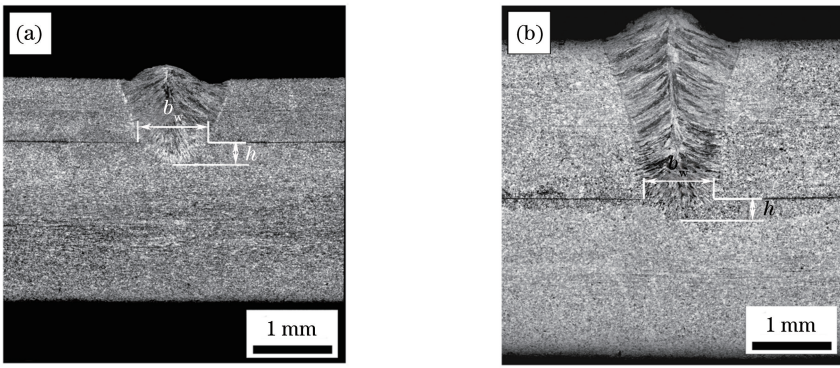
激光焊接接头的微观结构。(a) 0.8+2.0;(b) 2.0+2.0
